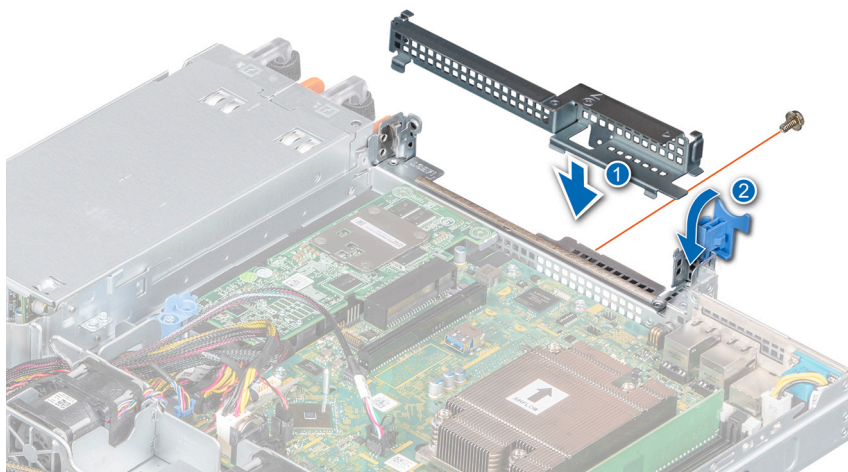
Installation de la plaque de recouvrement pour la carte de montage
